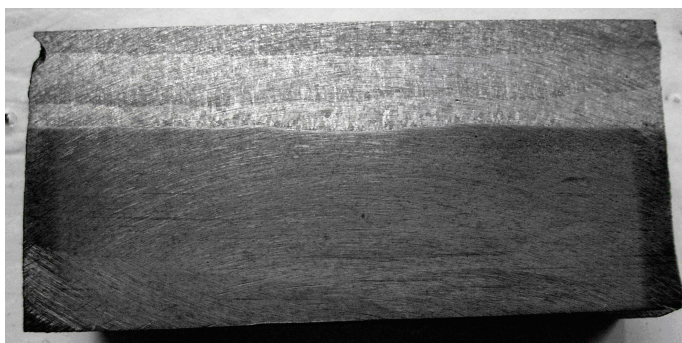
Макроструктура наплавленного и основного металла при использовании новой порошковой проволоки
